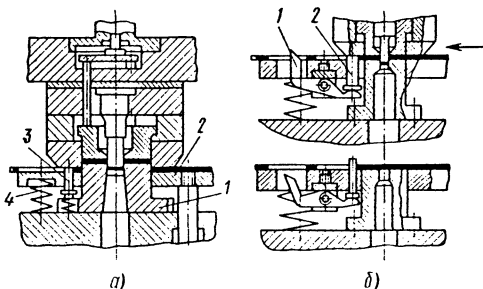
Схемы штампов для совмещенной вырубki и пробивки
